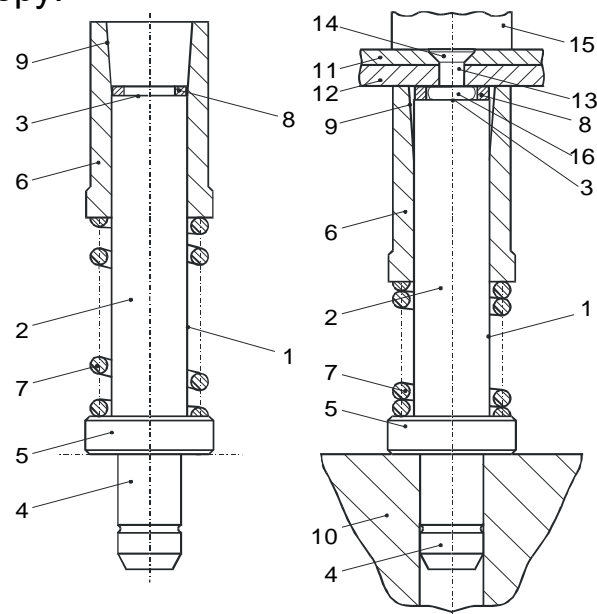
Конструкція штампа одиничного пресового клепаання
